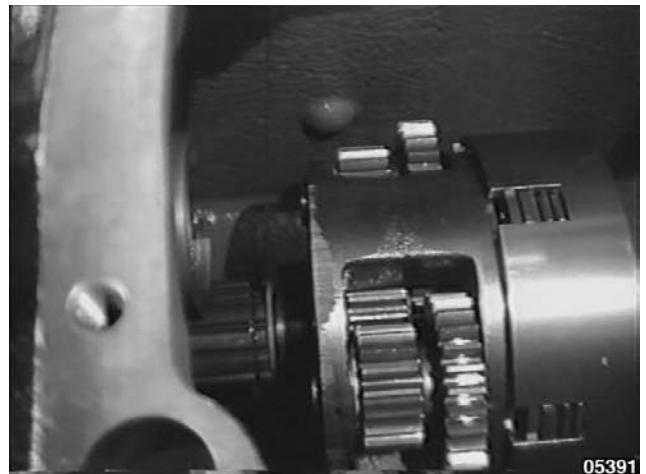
Ensemble Powershift monté dans le carter de boîte.
